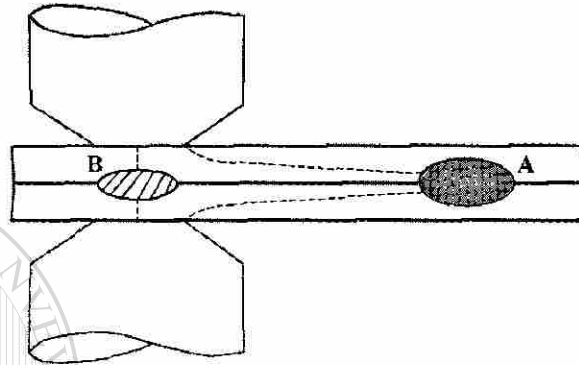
Efecto de desviación entre dos puntos de soldadura ⁽³⁷⁾.
